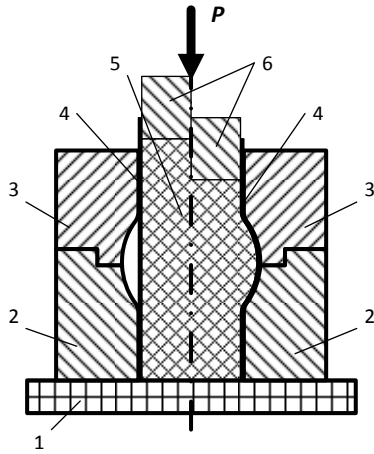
Схема раздачи трубчатой заготовки с использованием внутреннего наполнителя
